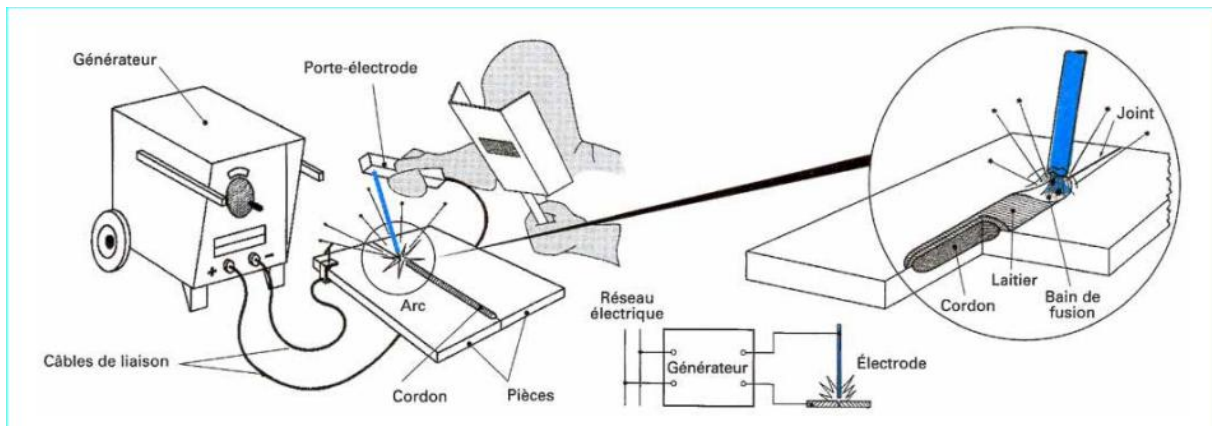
principe de Soudage à l'électrode enrobée.
